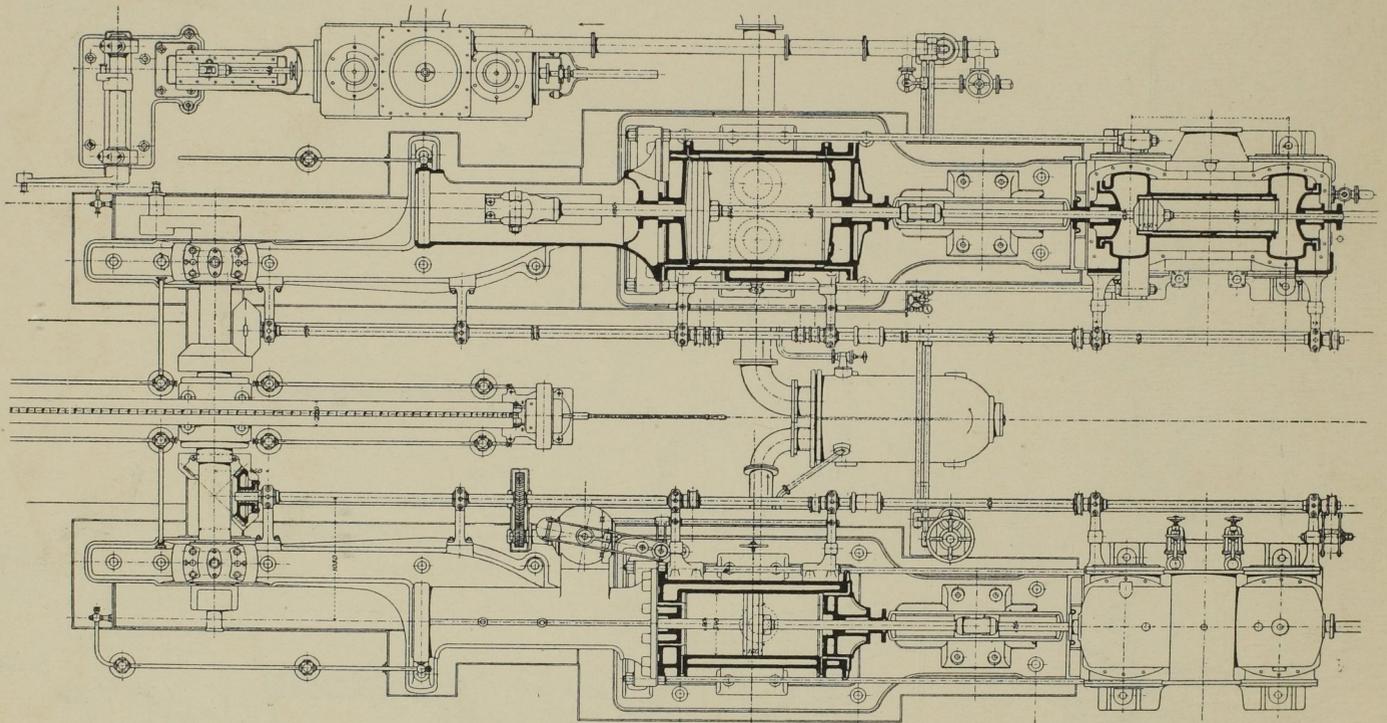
Grundriss der Pumpmaschine. Massst. 1 : 60.
